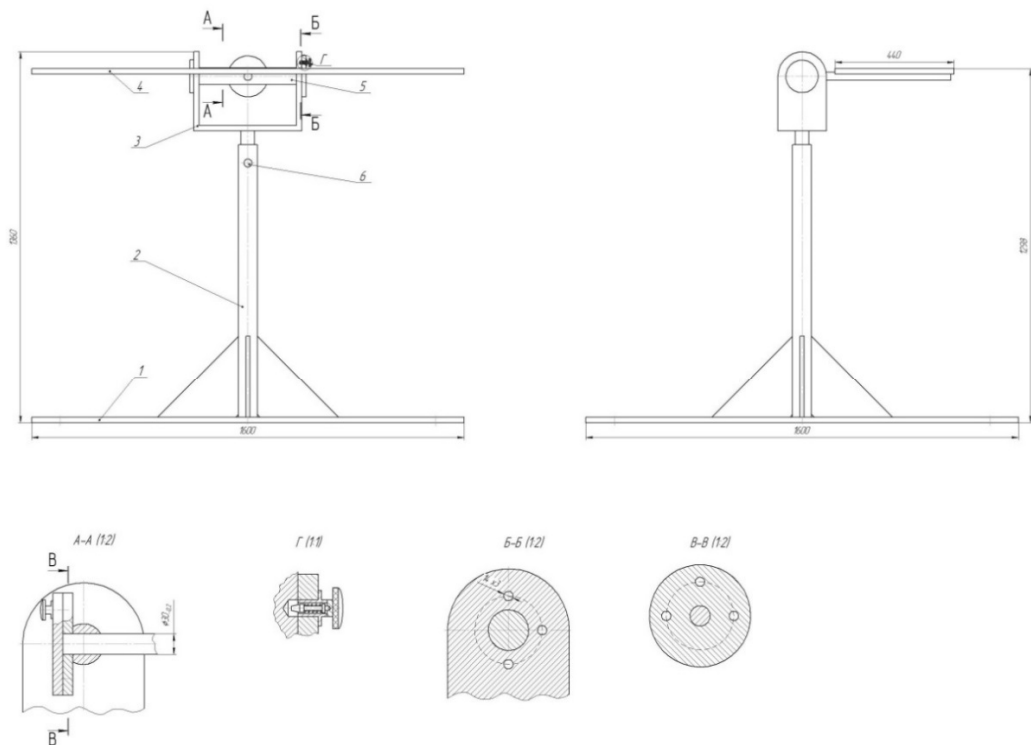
Спеціалізована пристосування для наплавлення ножа ковша грейфера: 1 - підстава; 2 - стійка; 3 - поворотний кронштейн; 4 - стіл; 5 - вісь; 6 - висувний упор
